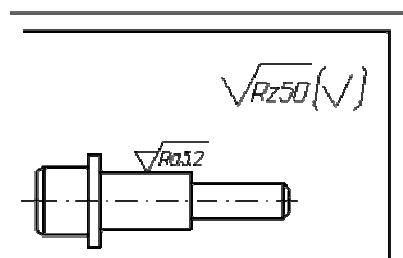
Указание шероховатости одинаковой для части поверхностей изделия
